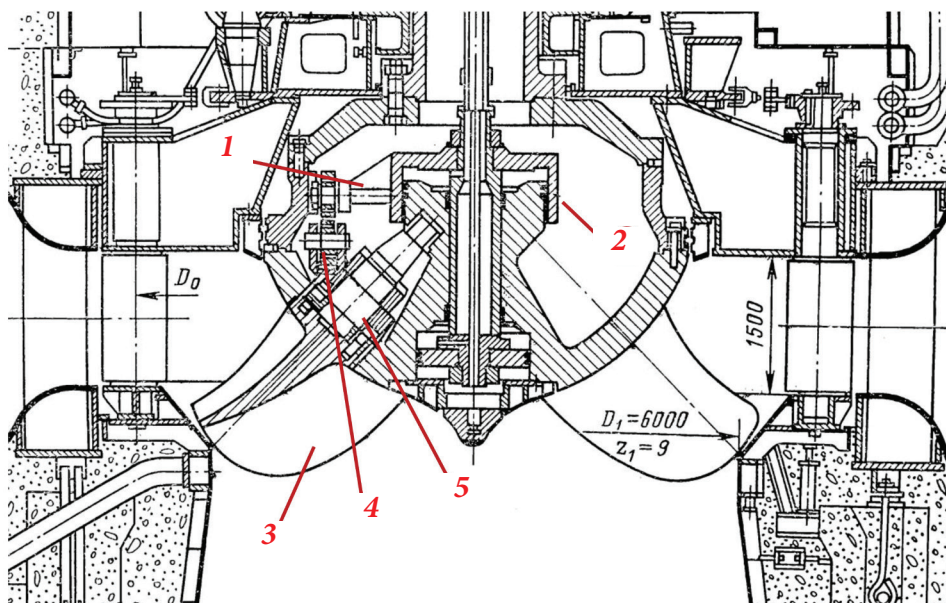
Фрагмент сборочного чертежа рабочего колеса: 1 – луч крестовины, 2 – цилиндрическая центральная часть крестовины; 3 – лопасть рабочего колеса; 4 – рычаг; 5 – цапфа
